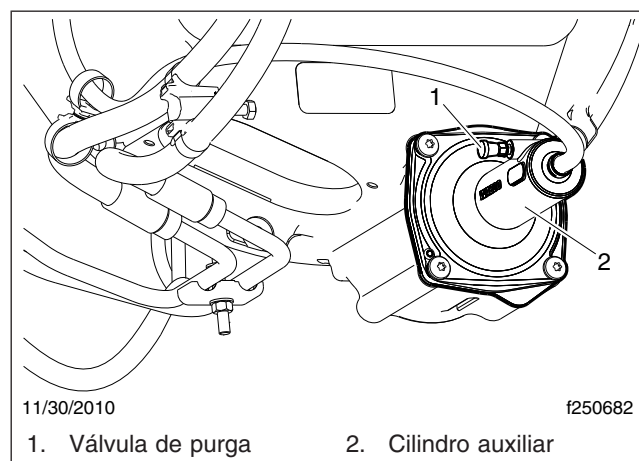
, Cilindro auxiliar, control del embrague hidráulico
